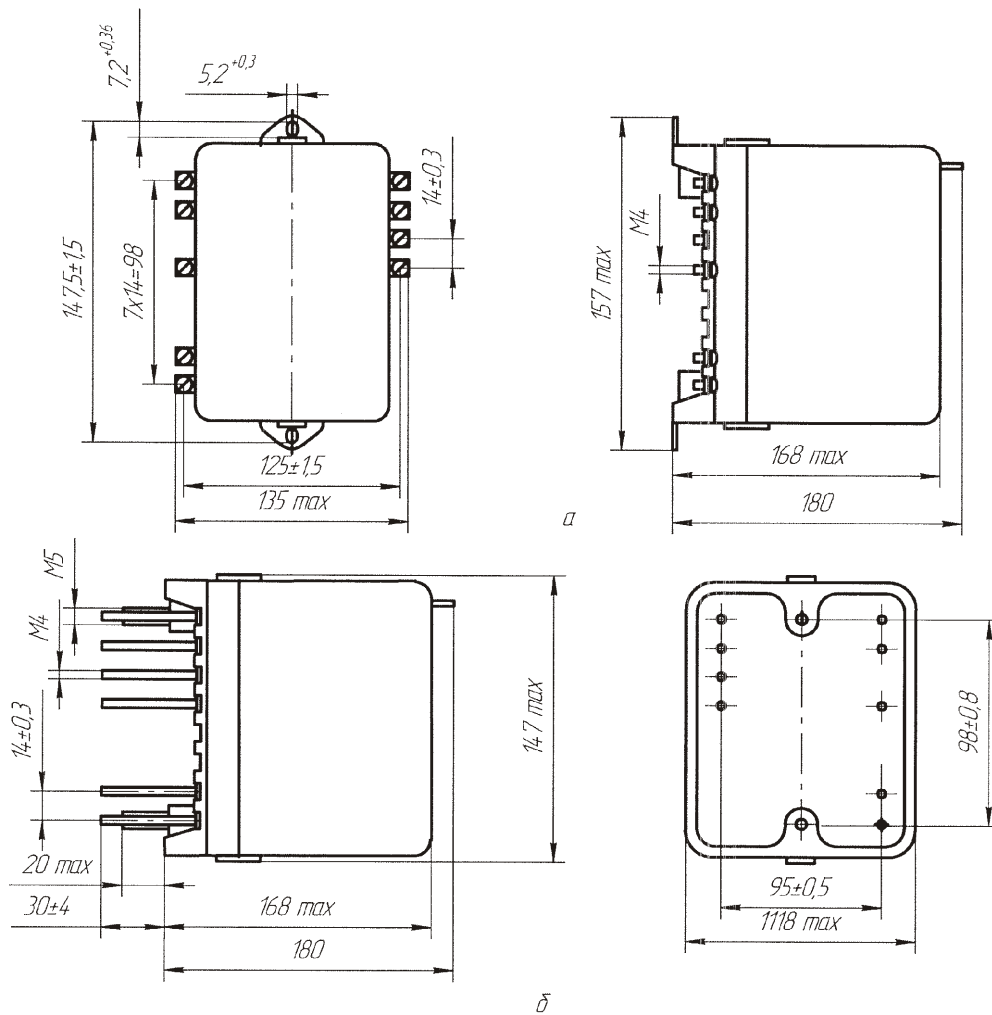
Габаритные, установочные и присоединительные размеры устройства типа УСЗ 2/2
